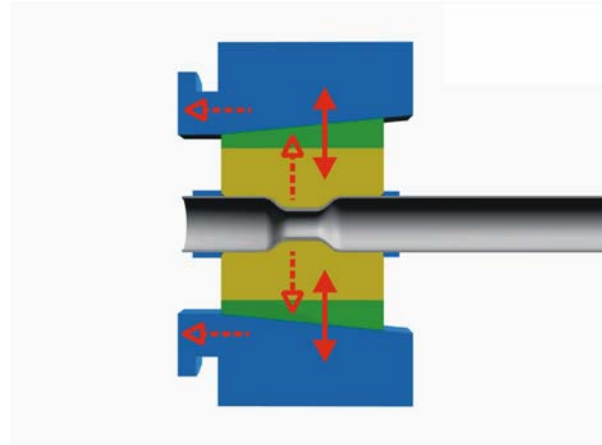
Einstechkneten – geschlossenes Werkzeug
